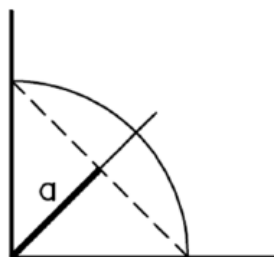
Triángulo isósceles que define el cordón de soldadura.
